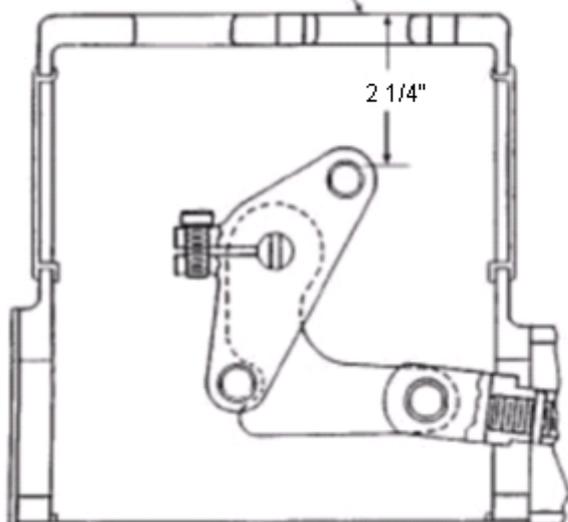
Положение рычага «воздух открывает». Размеры В и С
